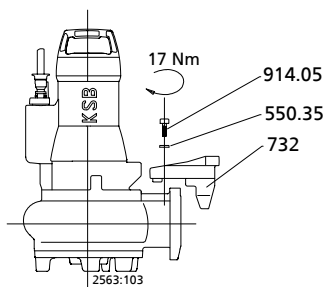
Установка крепеж-захвата при тросовых направляющих, 1 штанговой направляющей и хомуте.
